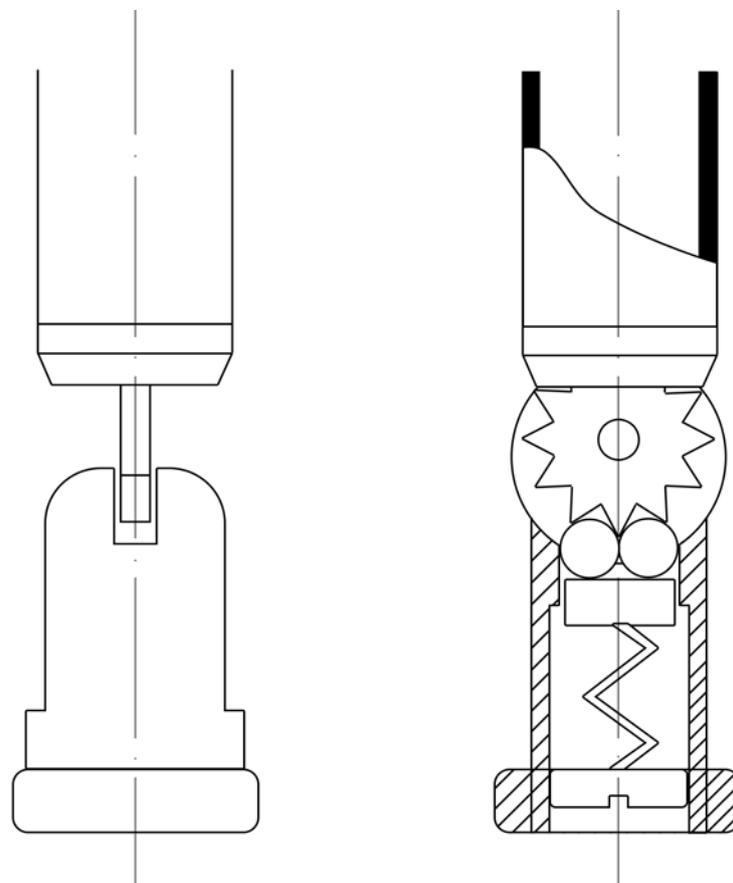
Узел крепления штыревой антенны — зубчатое колесо с двумя стальными шарнирами (авторское свидетельство 624 328)
